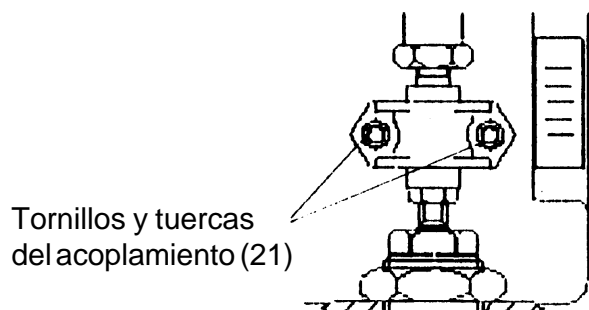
Conjunto de Adaptador del Actuador, Adaptador de la Válvula y acoplamiento
